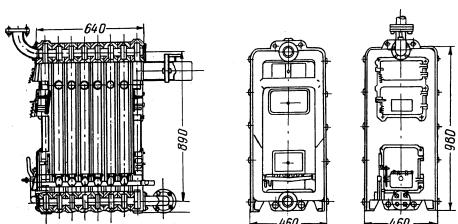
Габаритные размеры котла поверхностью нагрева 2,26 м<sup>2</sup>
